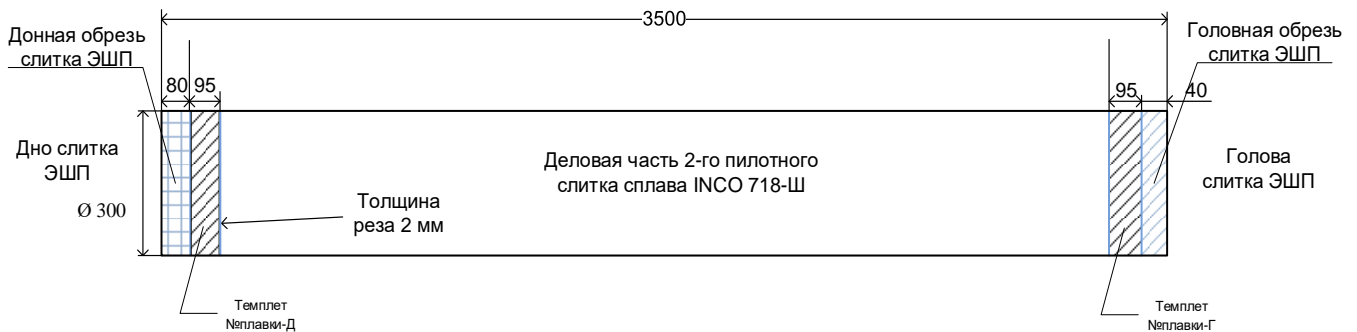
Схема порезки 2-го опытного слитка ЭШП сплава Inconel 718
